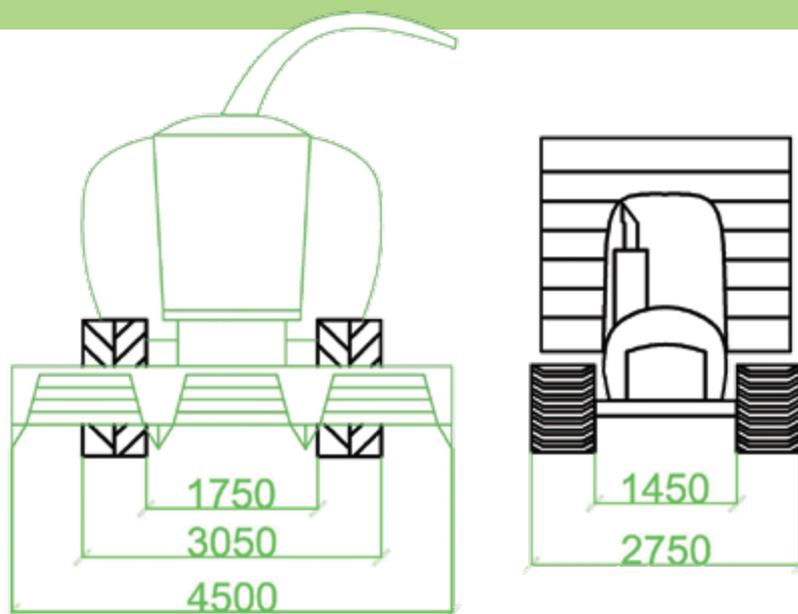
Габаритные размеры технологического комплекса машин для заготовки силоса
